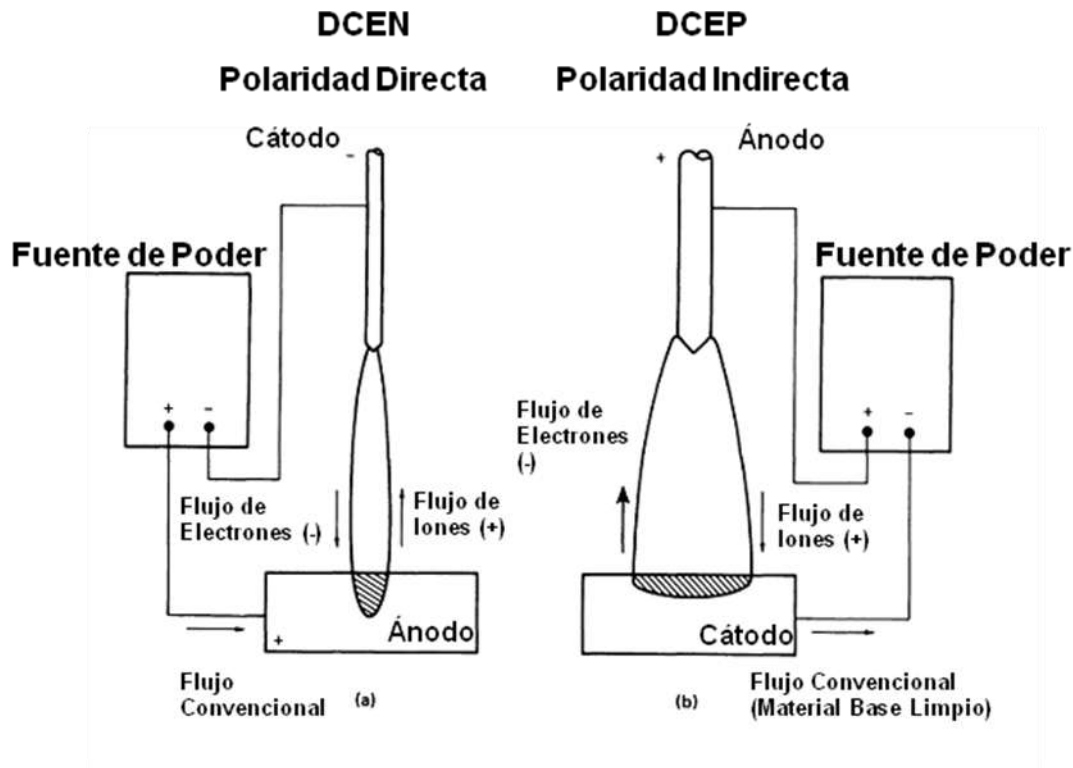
Efecto de la Polaridad en la configuración de soldadura TIG cuando se utiliza corriente directa.
